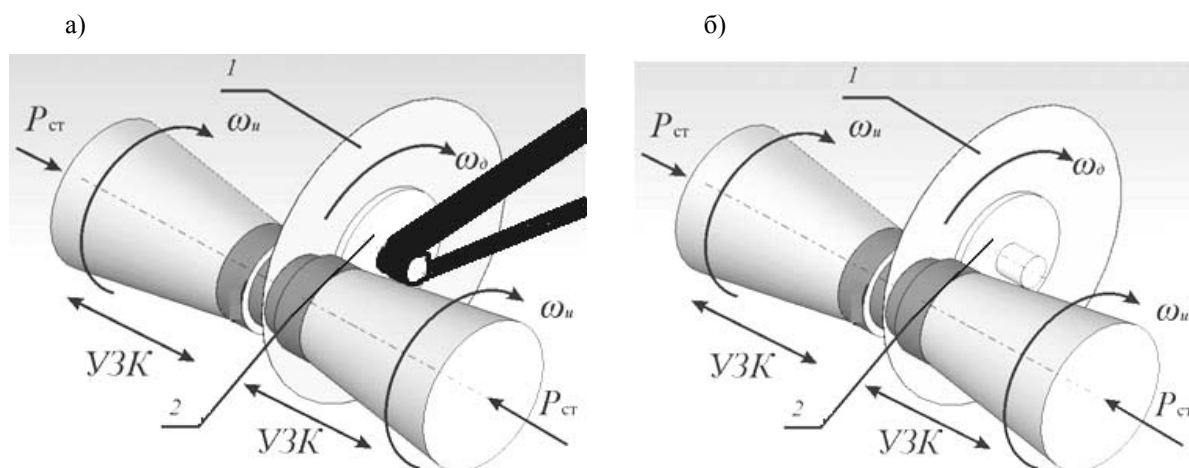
Технологическая схема шаржирования распиловочных дисков с ультразвуком по двухсторонней схеме: а – с вращением заготовки диска от отдельного привода; б – с вращением заготовки диска за счет фрикционной торцевой передачи
